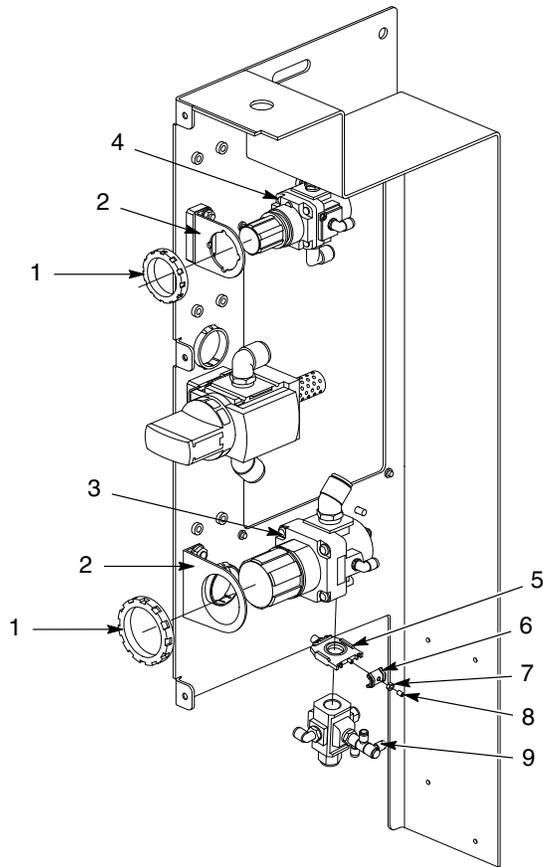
Dépose/remplacement du régulateur de Coulisseau en bas et du moteur pneumatique
